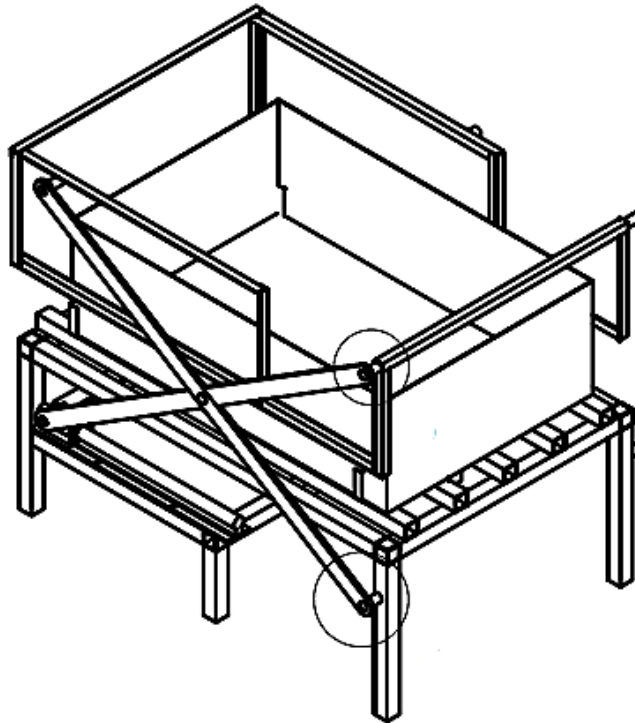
Ensamble de las piezas del sistema de elevacion.
